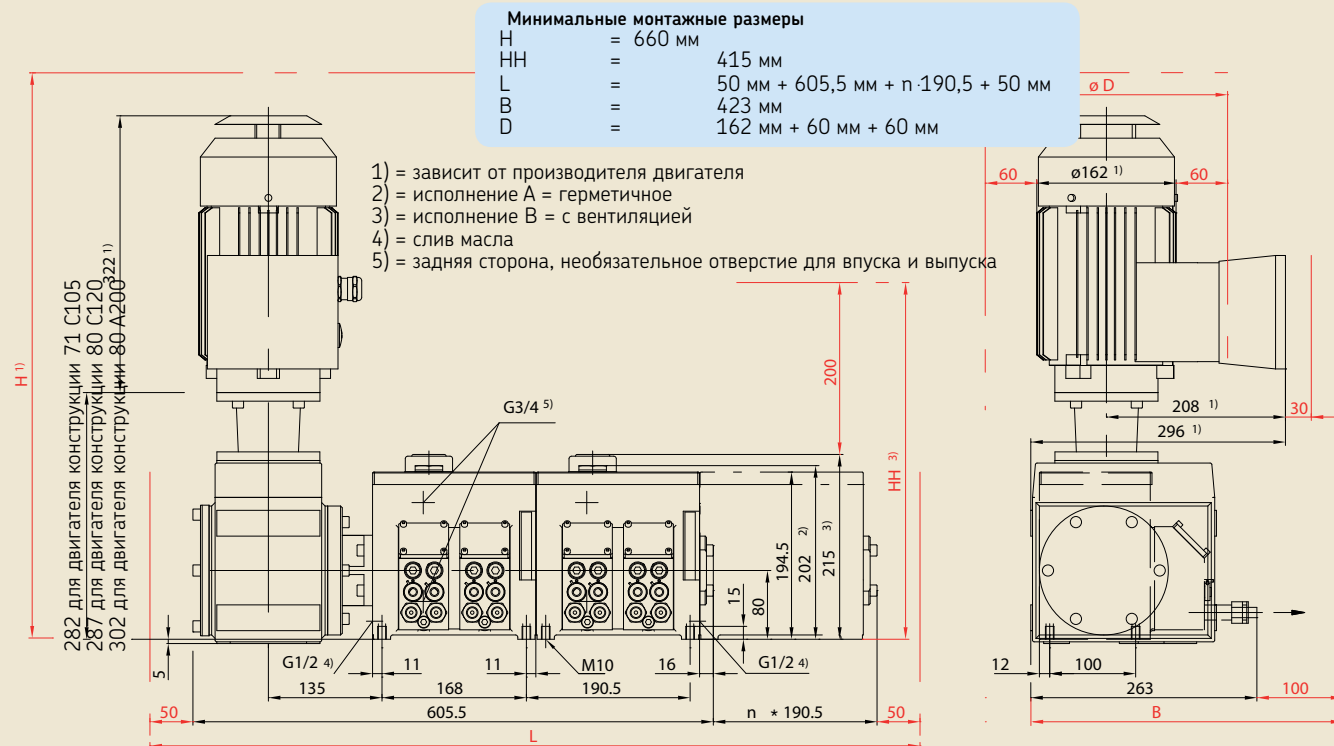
Монтажный чертеж, специальная версия, привод с редуктором
